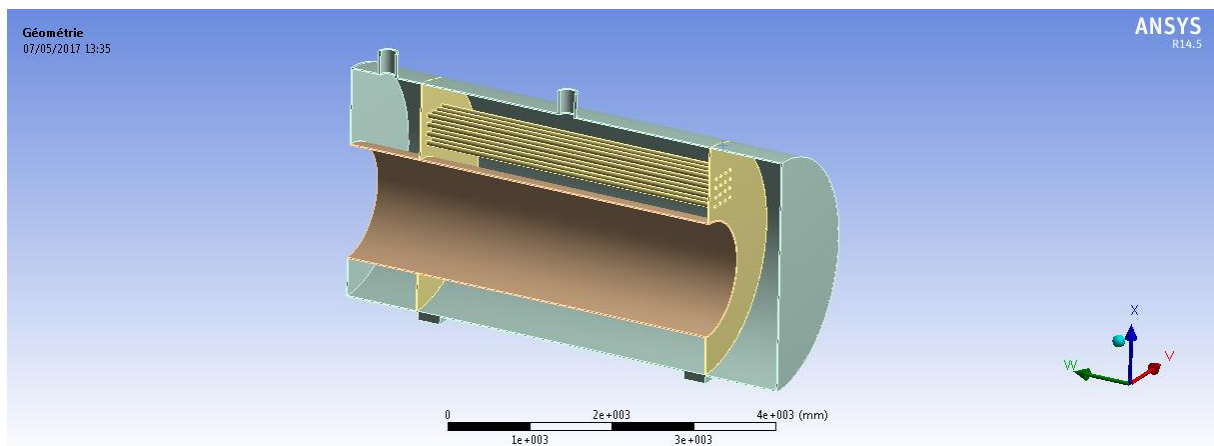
Vue complète d'un Model CAO d'une chaudière a tube de fumée
